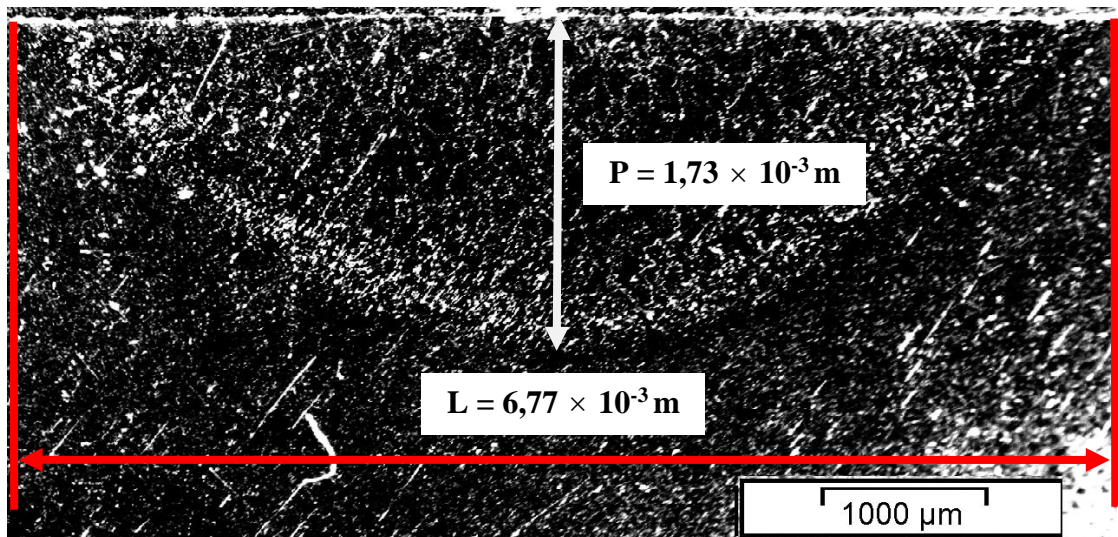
Largura e penetração do cordão de solda para condição de $t+ = 13 \text{ ms}$.
